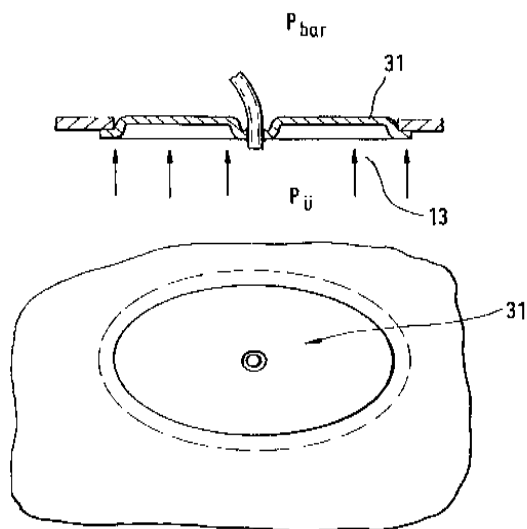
Полый корпус с крышкой по патенту US5632471A
